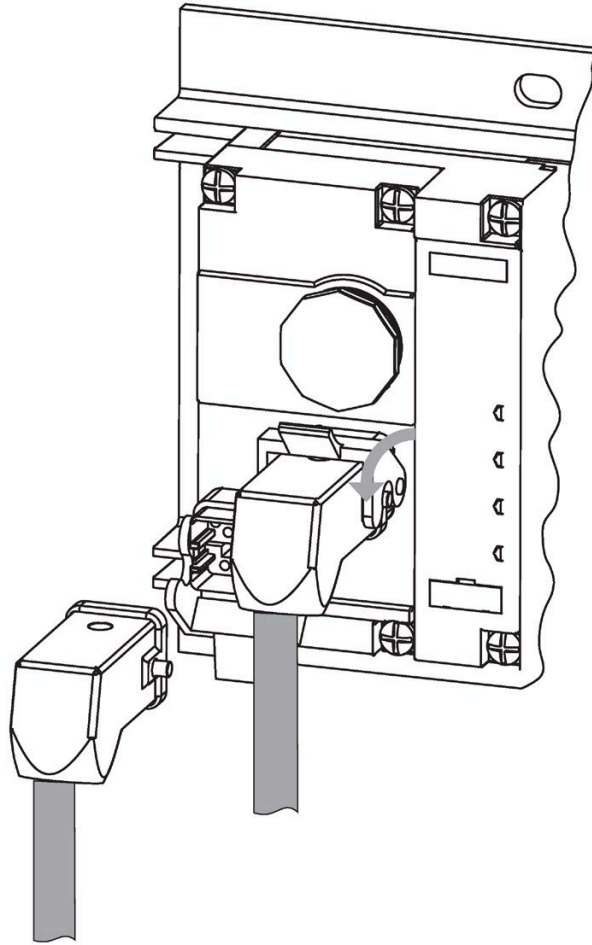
ECOFAST-Anschlusstecker anschließen
